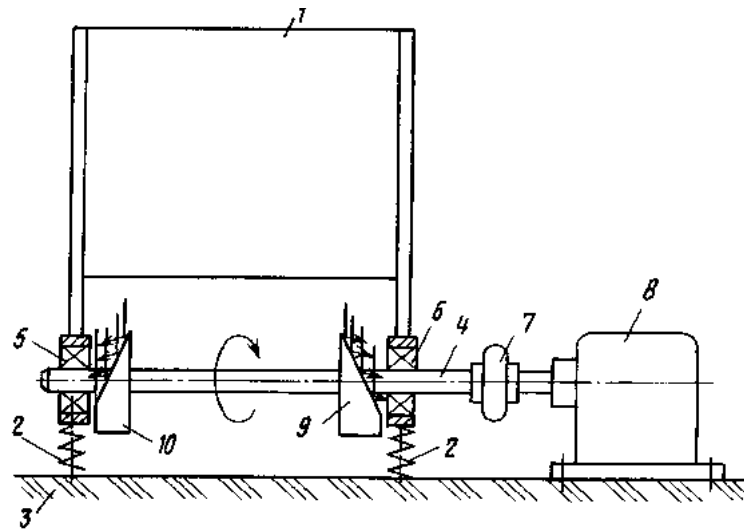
Пристрій для вібраційної оздоблювально-зміцнювальної обробки деталей: 1 – робоча камера; 2 – пружинні опори; 3 – нерухома основа; 4 – дебалансний вал; 5, 6 – підшипникові вузли; 7 – гнучка муфта; 8 – привод; 9, 10 – дебаланси
